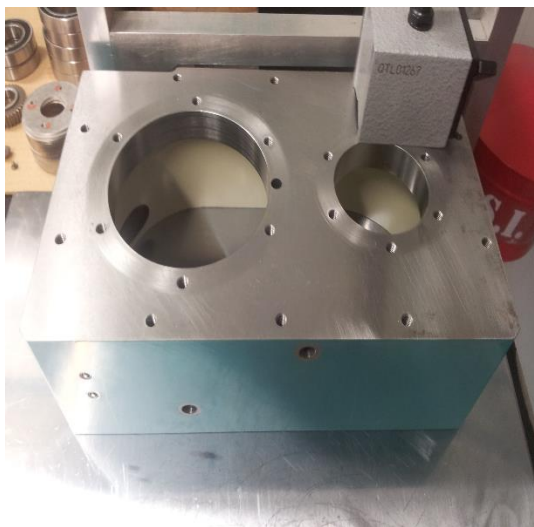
caixa do Gear box apos ter sido maquinada e pintada
